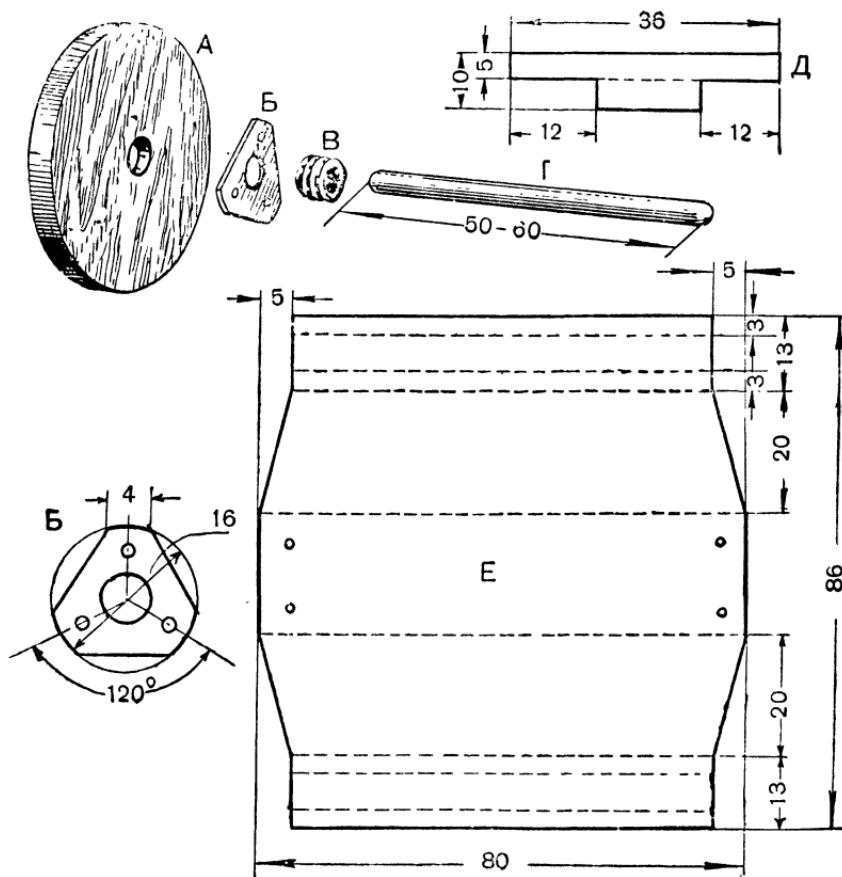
Детали редуктора № 3 (рис. 111): А — большой фрикцион; Б — жестяная накладка; В — подшипник; Г — вал; Д — развертка стяжки; Е — развертка корпуса.
